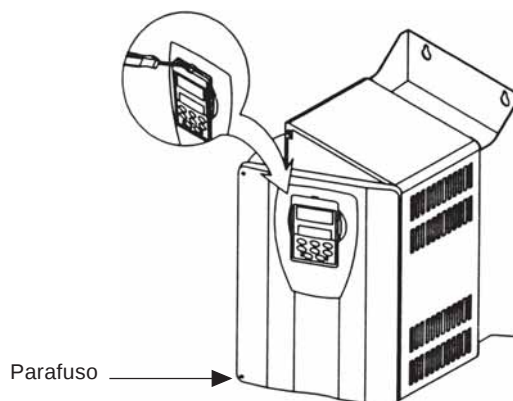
a) b) - Procedimento de remoção da HMI e tampa
